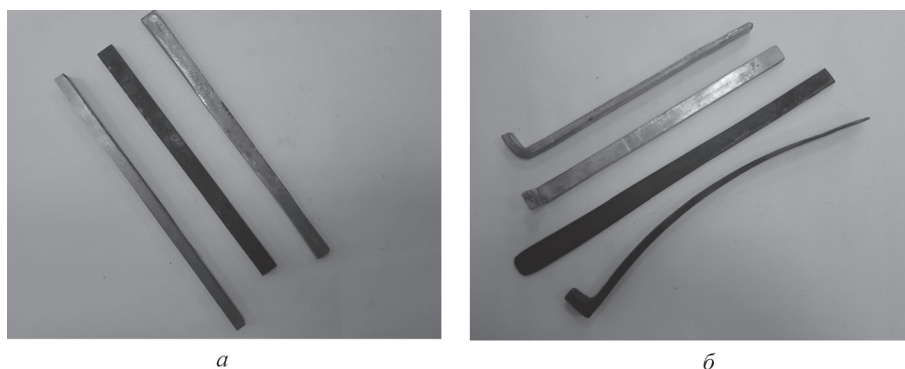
Внешний вид заготовок (а) и готовых изделий (б) полос переменной толщины
